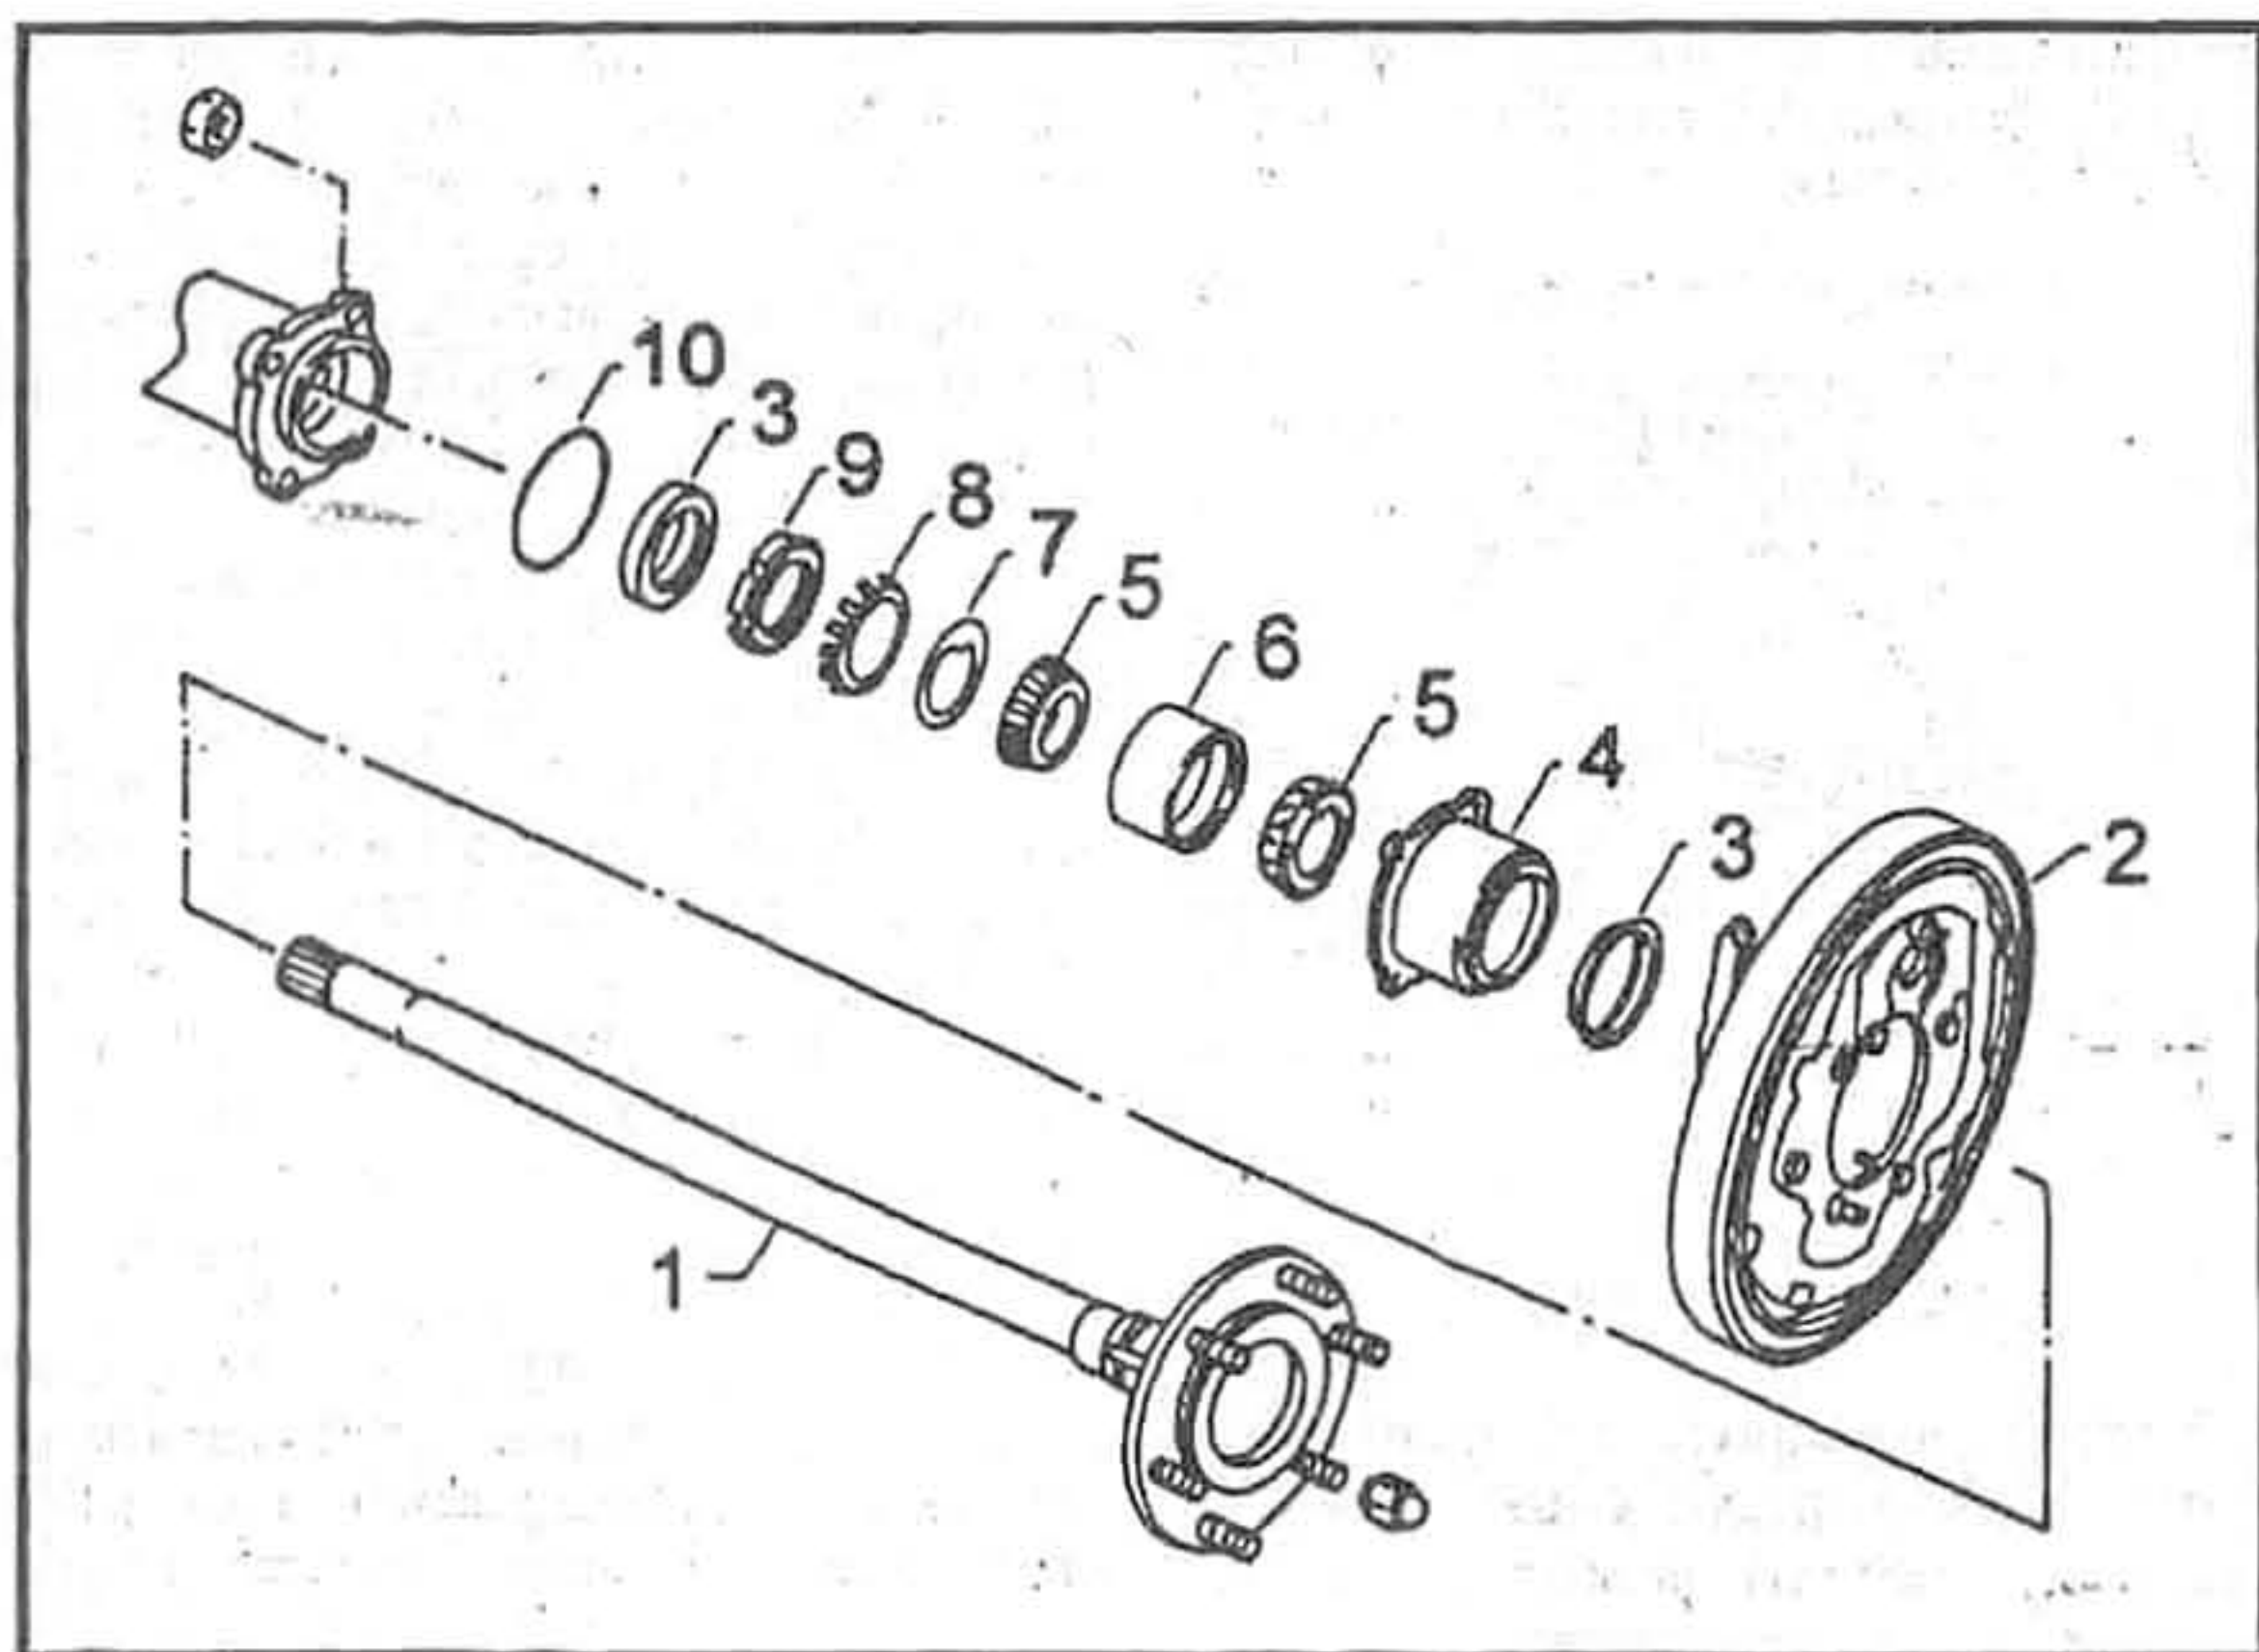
1. Полуось. 2. Опорный диск тормоза. 3. Сальник. 4. Корпус подшипника. 5. Подшипник. 6. Наружная обойма подшипника. 7. Шайба. 8. Стопорная шайба. 9. Стопорная гайка. 10. Уплотнительное кольцо.
